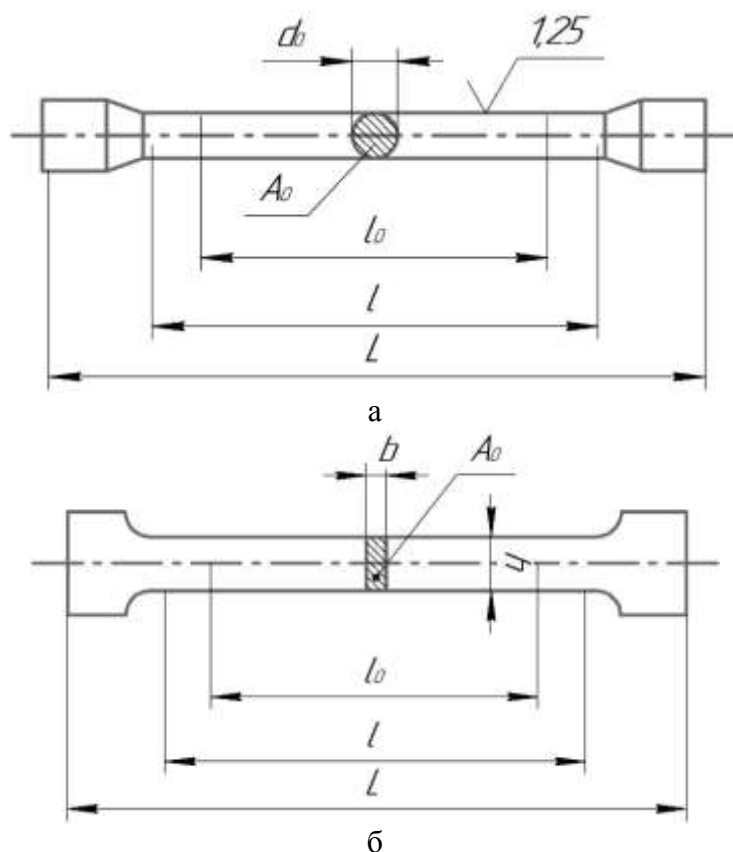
Эскизы испытательных образцов: а – цилиндрический образец; б – плоский образец
